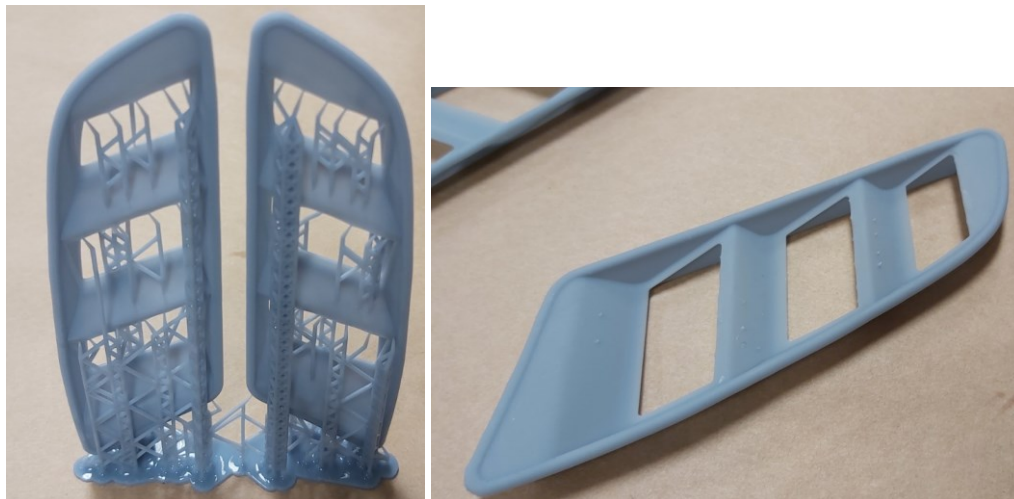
Již vytisknuté a uvolněné pouzdro od podpěr.
